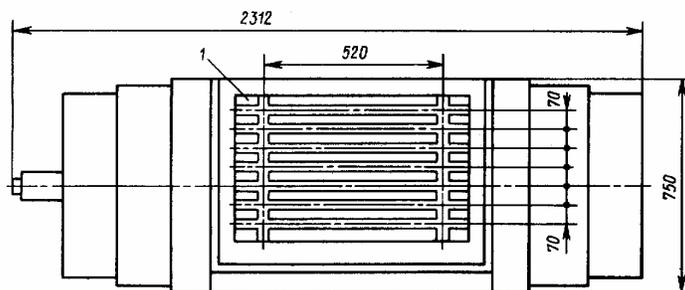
Параметры крестового стола сверлильно-фрезерно-расточного станка мод 2254ВМФ
